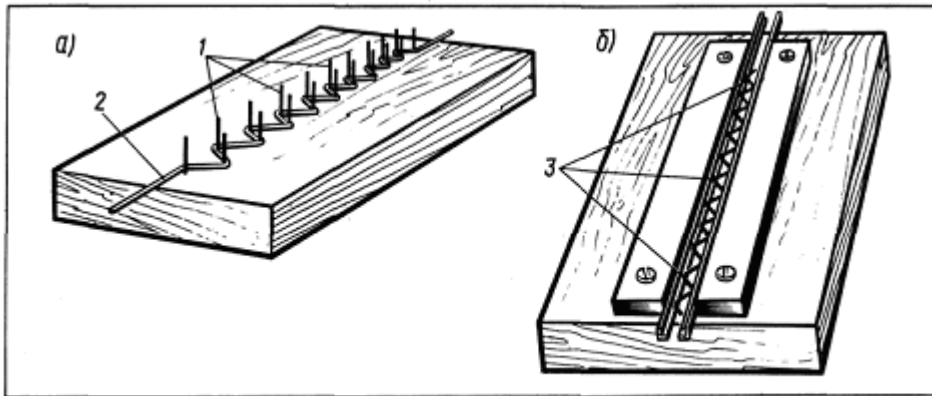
Шаблон для изготовления решетки (а) и кондуктор для сборки семафорной мачты (б)
